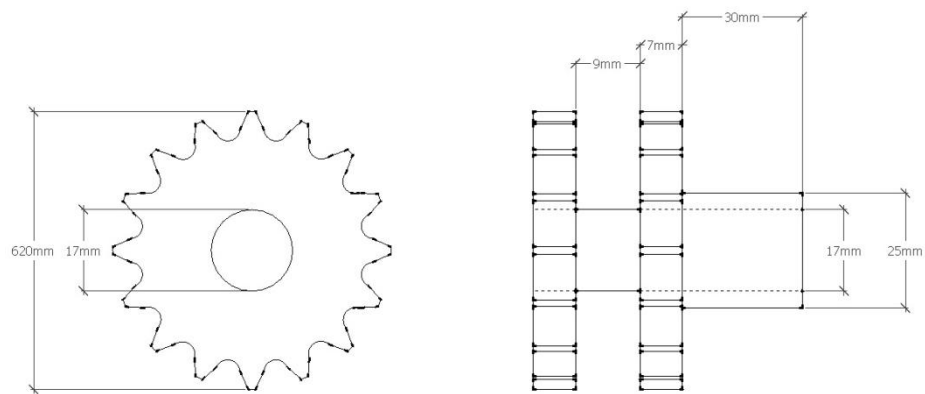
Spesifikasi Ukuran Pada Bearing
